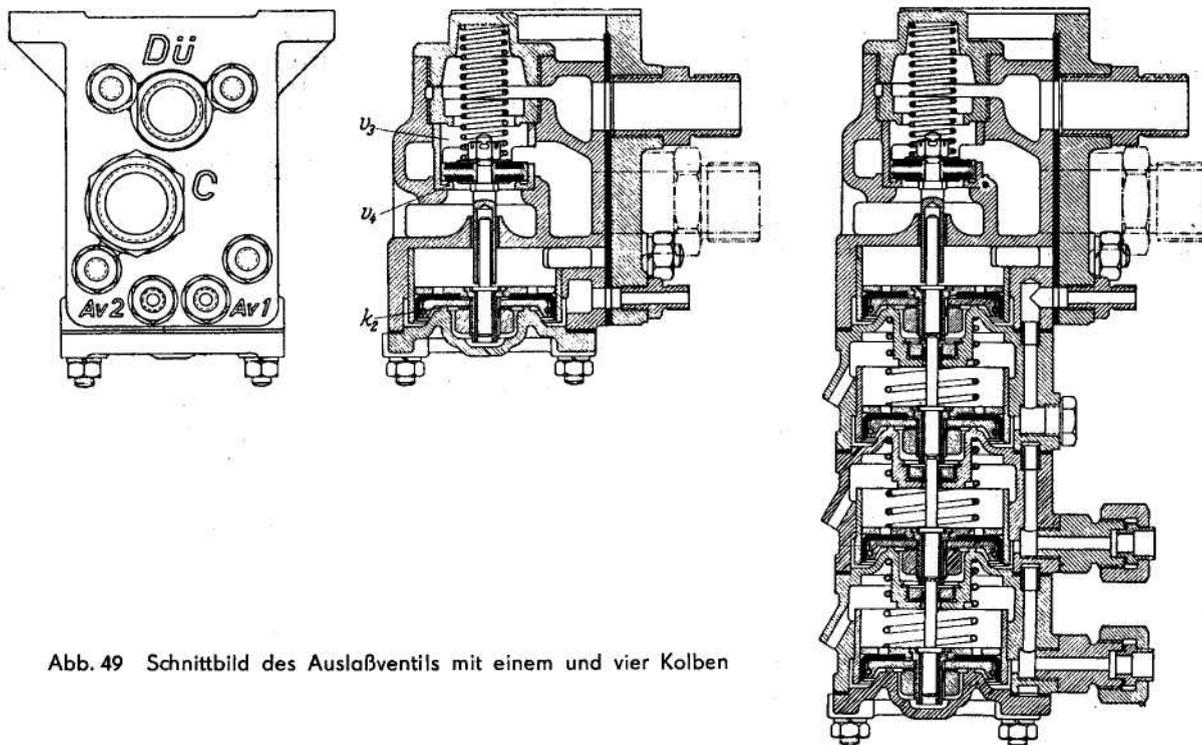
Schnittbild des Auslaßventils mit einem und vier Kolben
